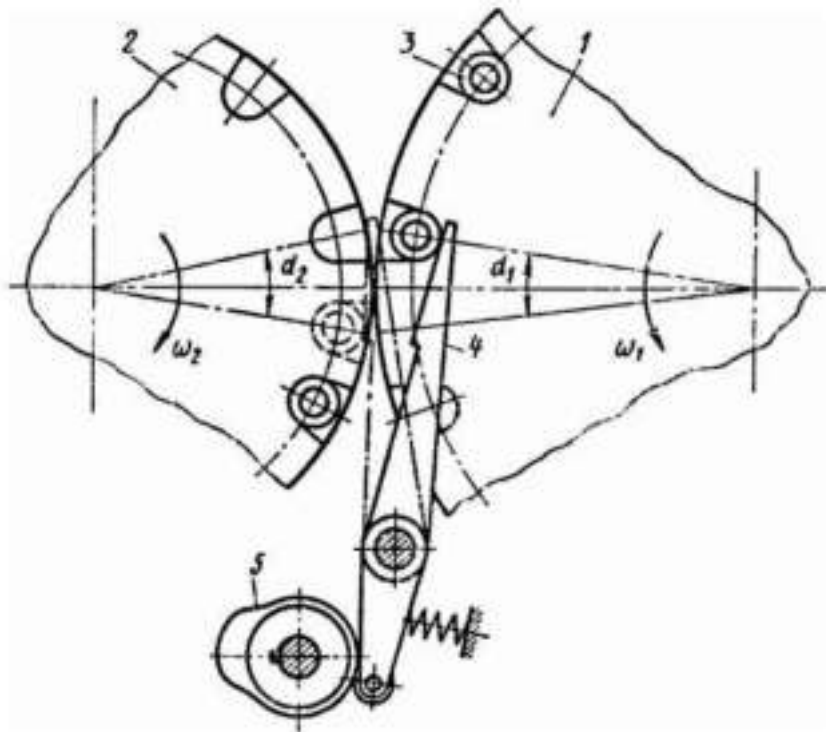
Ператалкиватель: 1, 2 – роторы; 3 – обрабатываемое изделие; 4 – рычаг; 5 – кулачок
